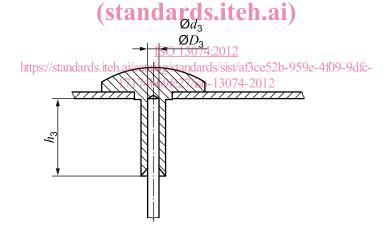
Dimensions d'ajustement de la roue des secondes et de l'aiguille des secondes
